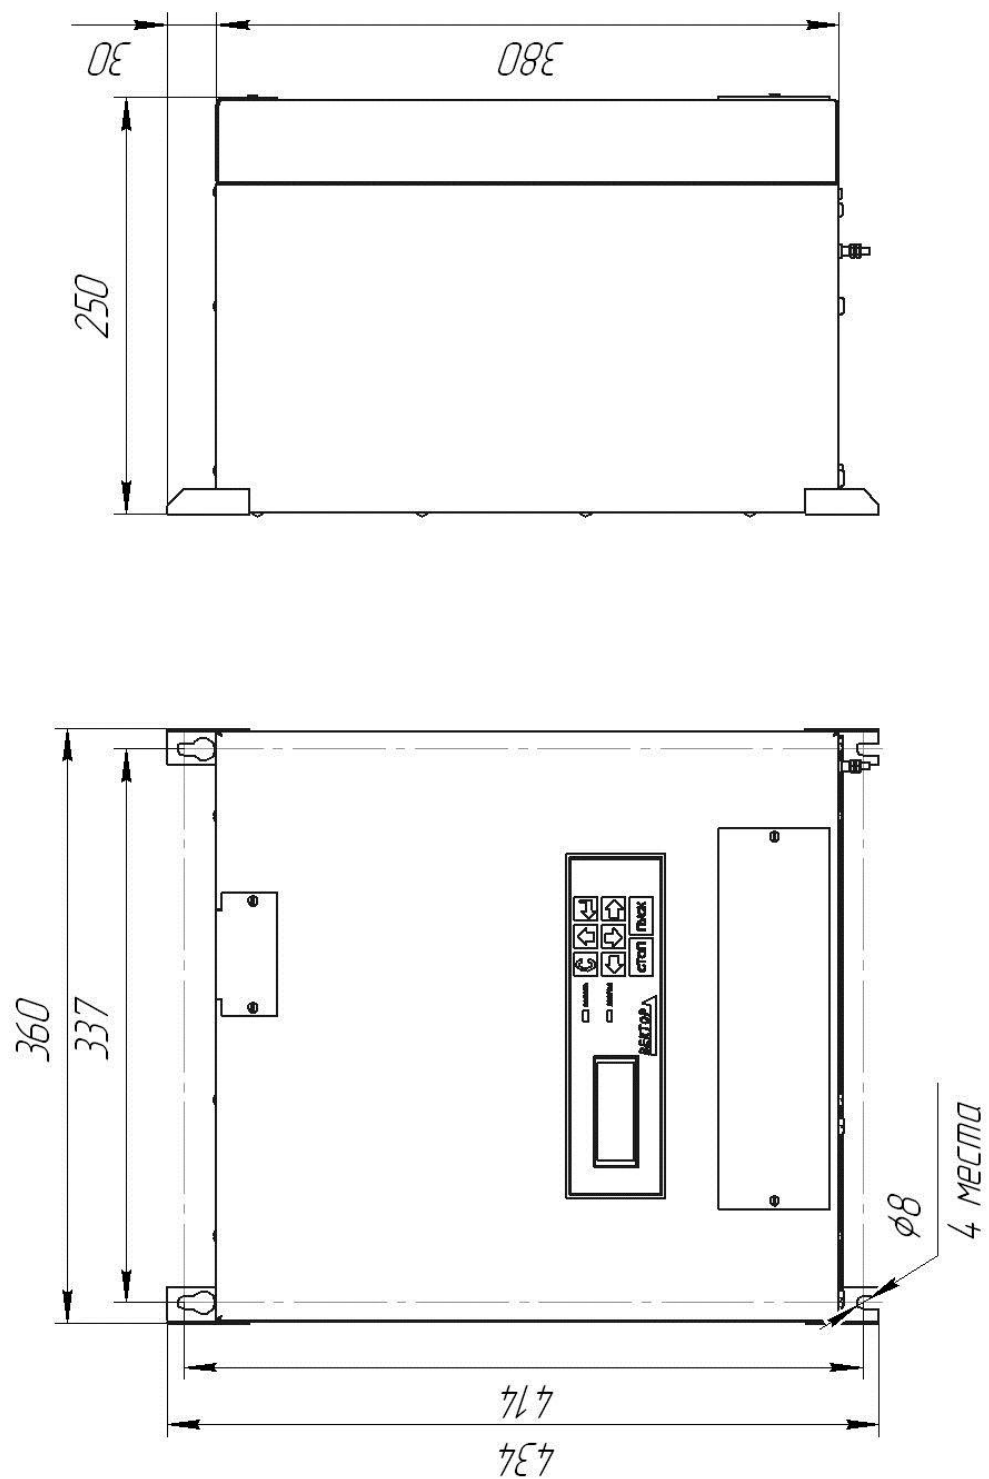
в Габаритные и установочные размеры ЭП-ПП-00 380/250
